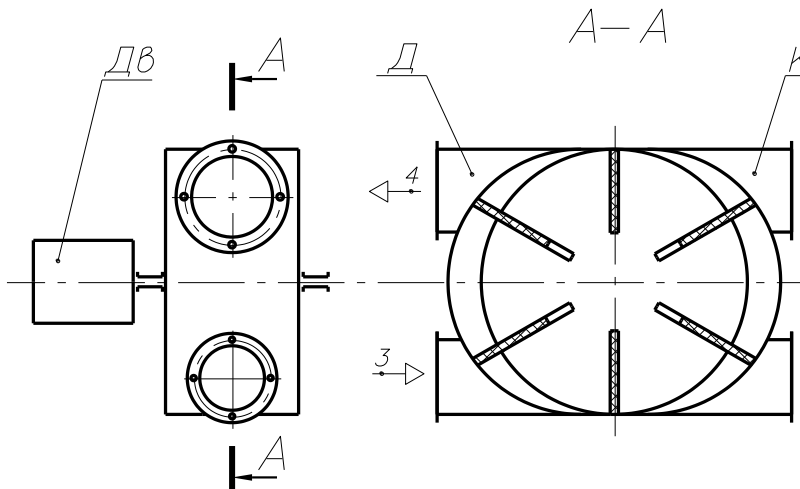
Компресорно-детандерний агрегат суміщеного виконання робочих порожнин:
